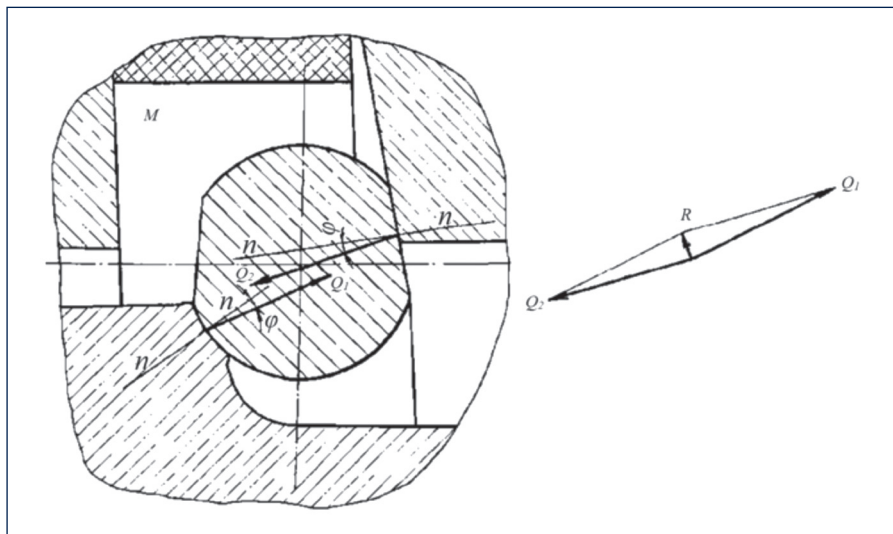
Положение деталей соединения Р-200 при нагружении внутренним давлением
